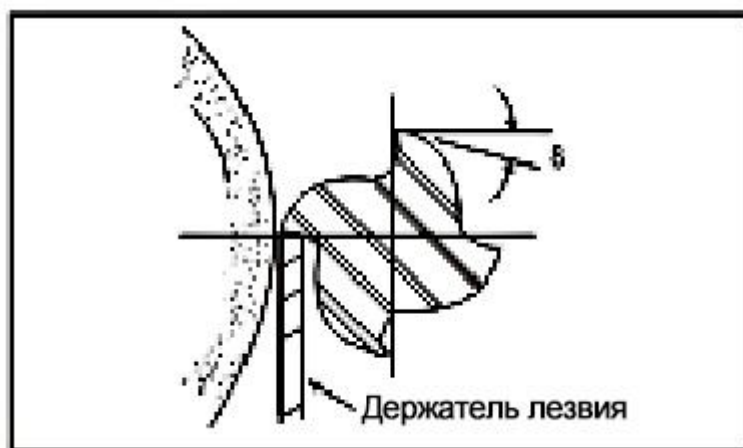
Высота центра шлифовального круга и центра режущего инструмента при рецессивном шлифовании
